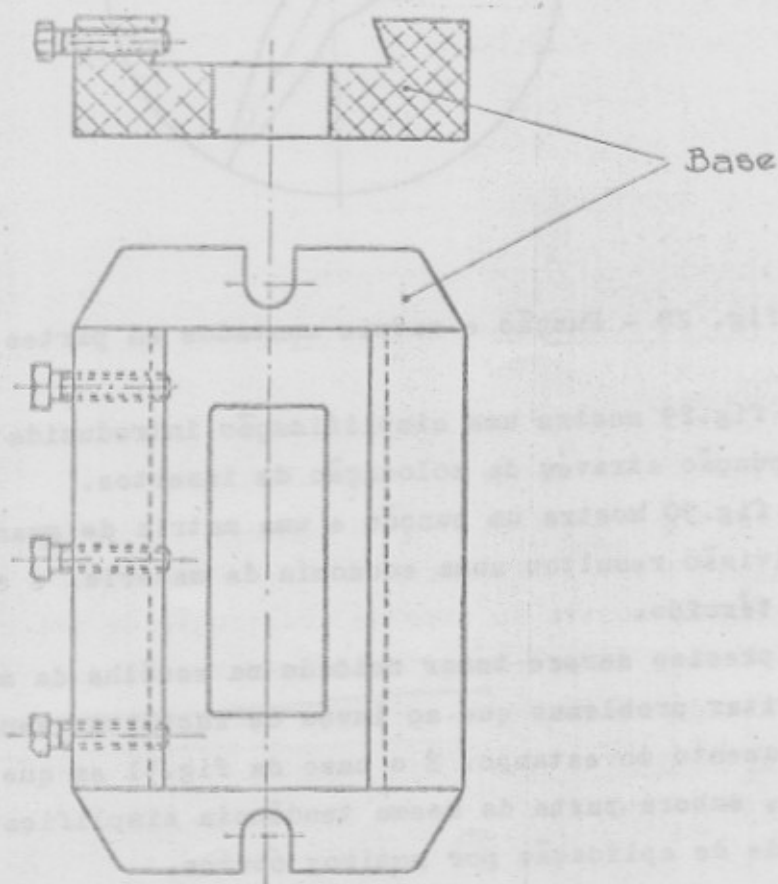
Fixação de uma placa de corte com encaixe do tipo prismático
